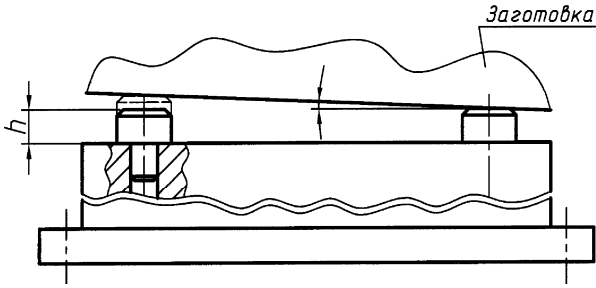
Формирование погрешности изготовления и сборки установочных элементов
